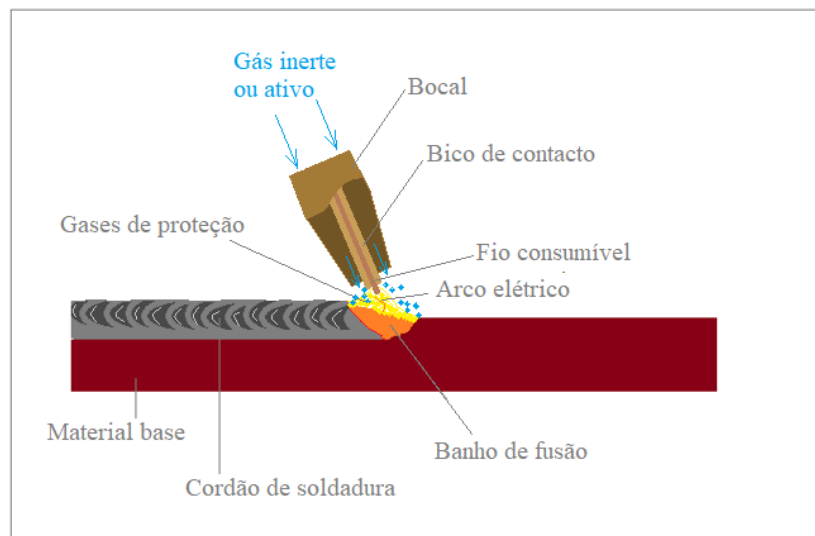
Ilustração da soldadura MIG/MAG – [10] Imagem adaptada
